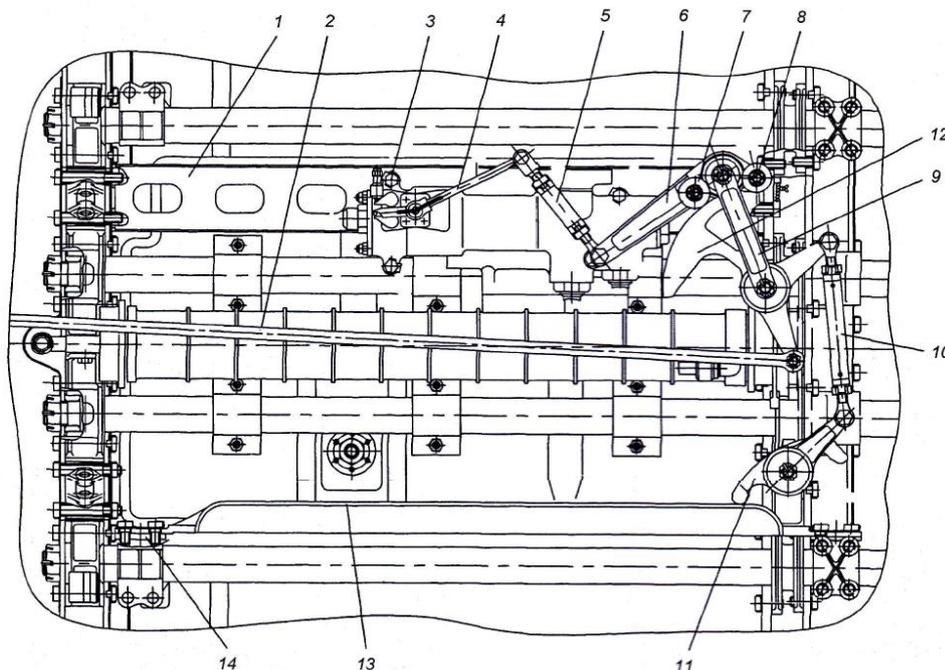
Механизм управления и блокировки РУ двигателя ПС-90А
